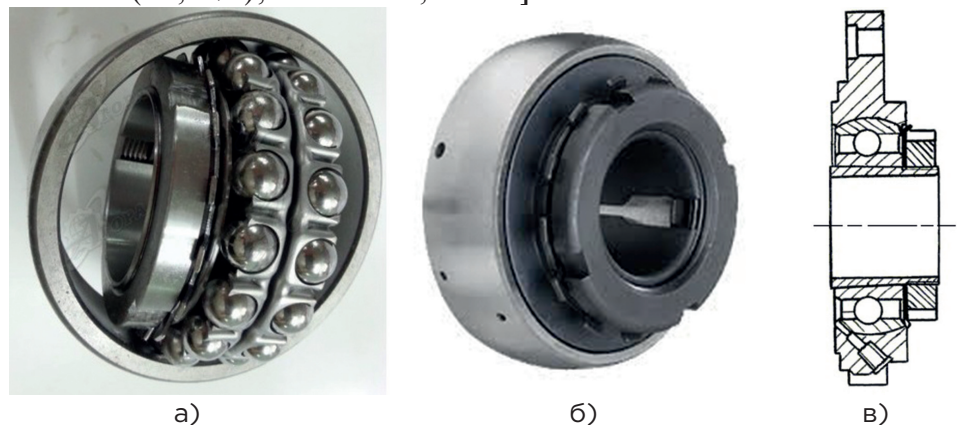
Конструкційні відмінності типів підшипників, які застосовуються в опорах молотильних барабанів зернозбиральних комбайнів а – дворядний радіальний підшипник № 11312; б - однорядний радіальний підшипник № 680314НК7С17; в - креслення підшипникової опори молотильного барабана
